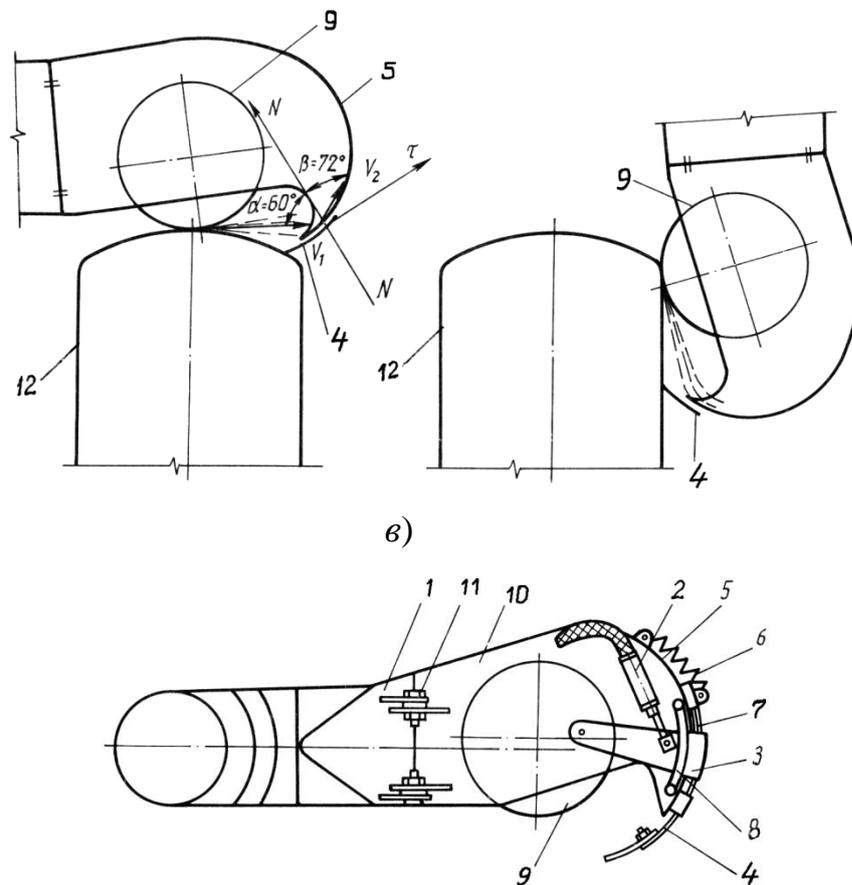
Устройство отсоса пылеприёмника шероховального станка: *а* – обработка верхней части шины; *б* – обработка боковой части шины; *в* – устройство пылеприёмника.
